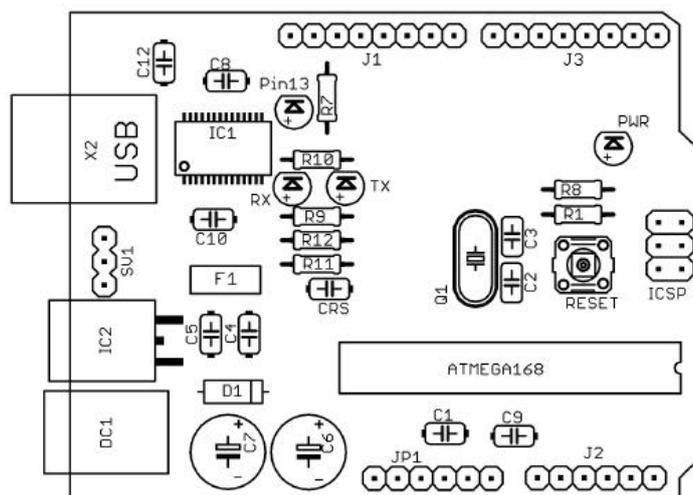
Схема сборки Freeduino Through-Hole Kit
